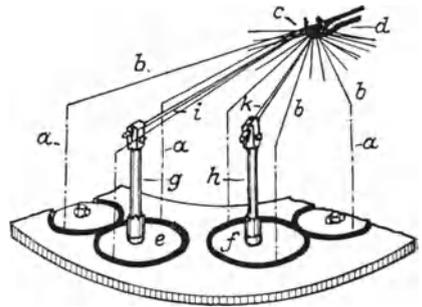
Endteller mit aufgeschraubten Flechtfedern.
